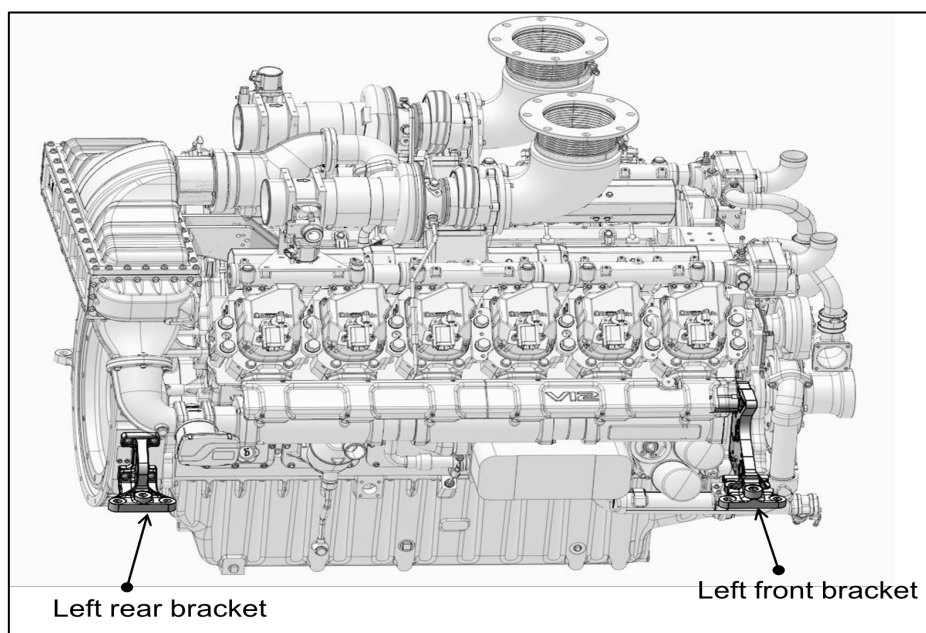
В – Опоры крепления двигателя, левая сторона
